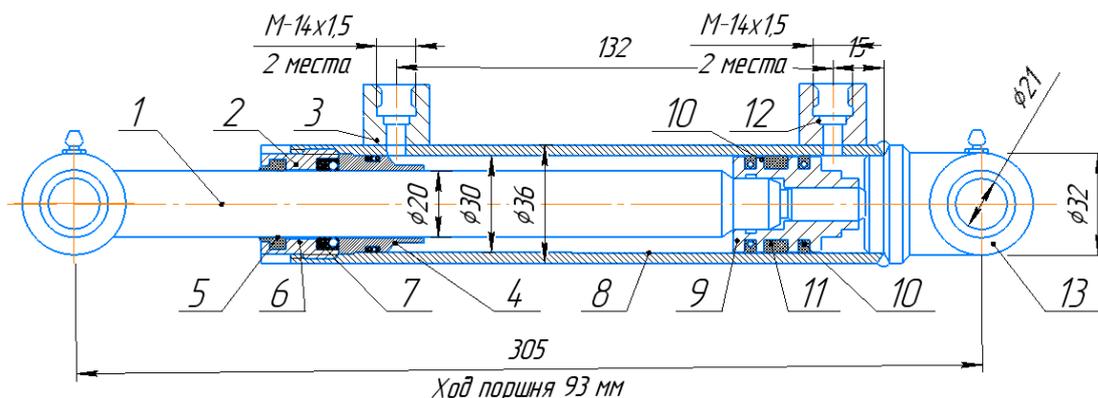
Чертеж гидроцилиндра: 1 – шток; 2 – гайка; 3 – штуцер; 4 – втулка; 5 – грязесъемник; 6 – гайка; 7 – манжета; 8 – корпус гидроцилиндра; 9 – поршень; 10 – манжета; 11 – кольцо; 12 – штуцер; 13 – проушина
